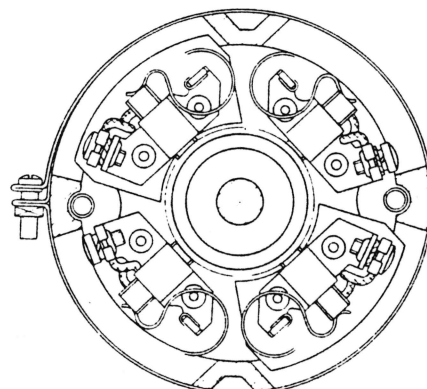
Querschnitt durch das Kollektorlager mit Ansicht der Bürsten.
